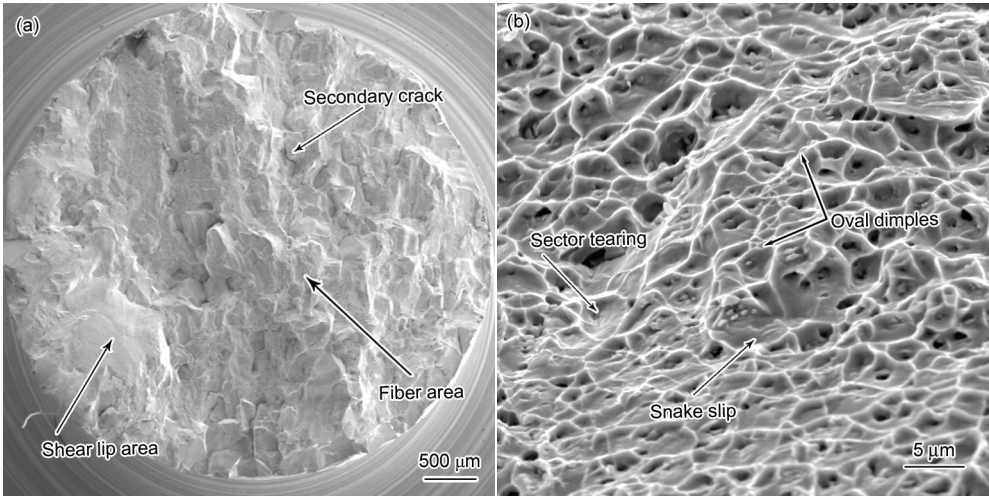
激光立体成形 Inconel 718 合金热处理态的拉伸断口形貌
